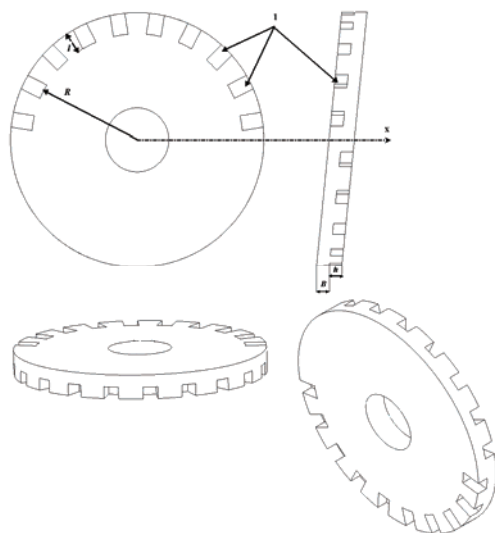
Конструкция самоосциллирующего круга с прерывистой режущей поверхностью.
